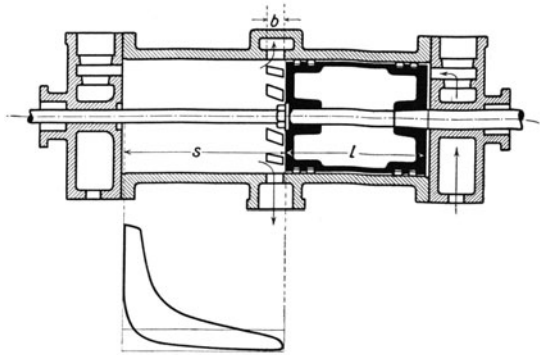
Steuerung mit Auspuffschlitzen. Gleichstromdampfmaschine.
